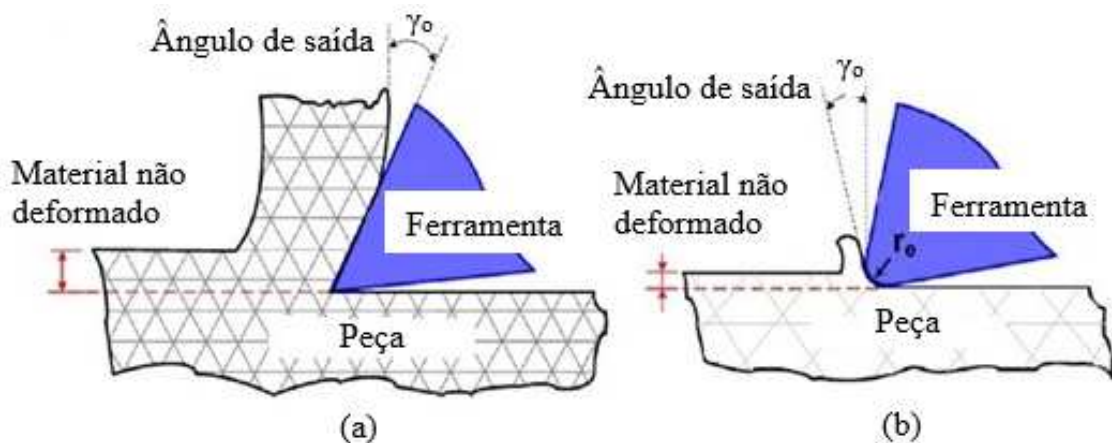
Desenho esquemático.(a) Usinagem convencional macro escala; (b) microusinagem.
